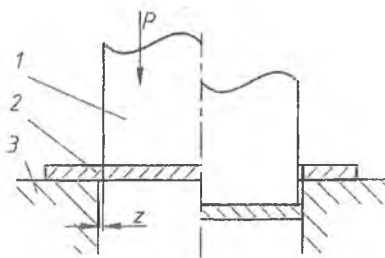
Схема операции вырубki заготовки из листа: 1 – пуансон, 2 – заготовка, 3 – матрица
